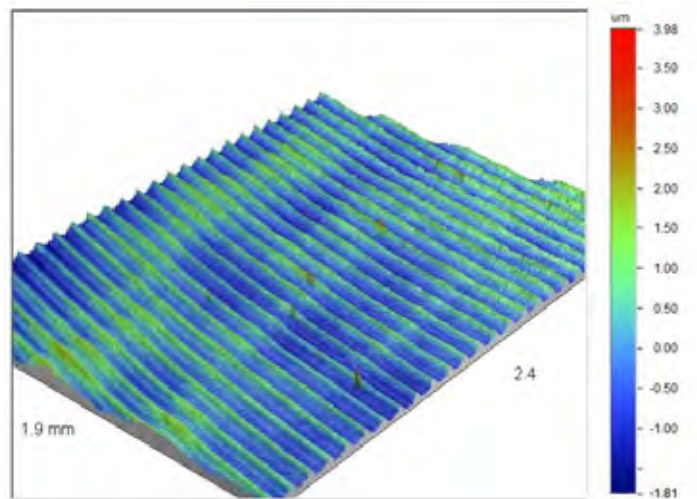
Representação tridimensional da superfície do material GUF, usinado sob condição C3.
